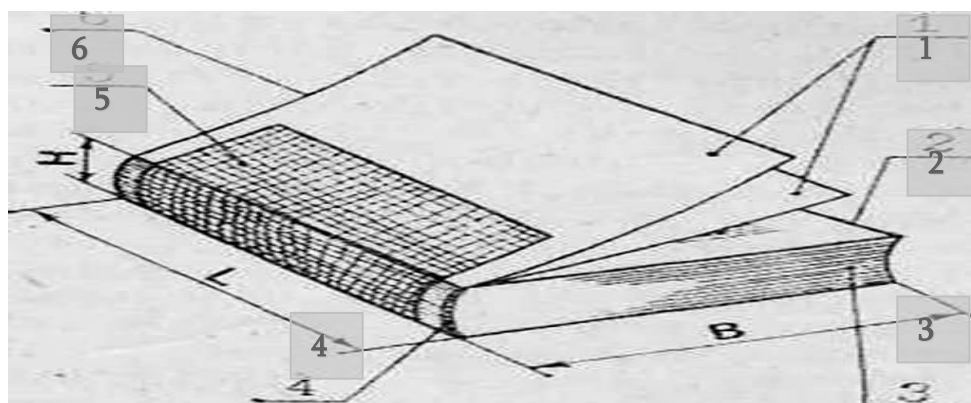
Книжковий блок: 1 – форзац; 2 – передній обріз блока; 3 – нижній обріз блока; 4 – каптал, 5 – марля; 6 – верхній обріз блока; В – ширина блока; L – довжина блока (висота); Н – товщина блока
